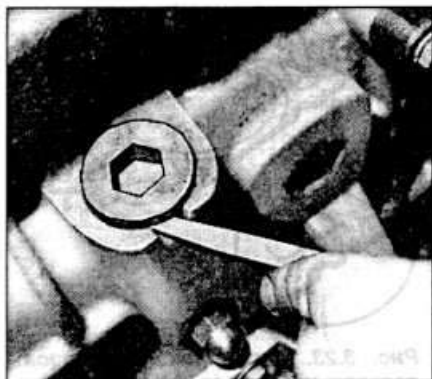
Проверка зазора между опорной поверхностью заглушки корпуса масляного насоса и поверхностью блока цилиндров
